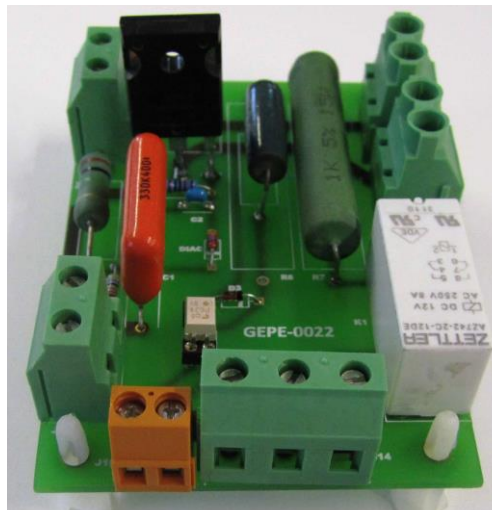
PCB com circuito de proteção do barramento CC para 900 V.
